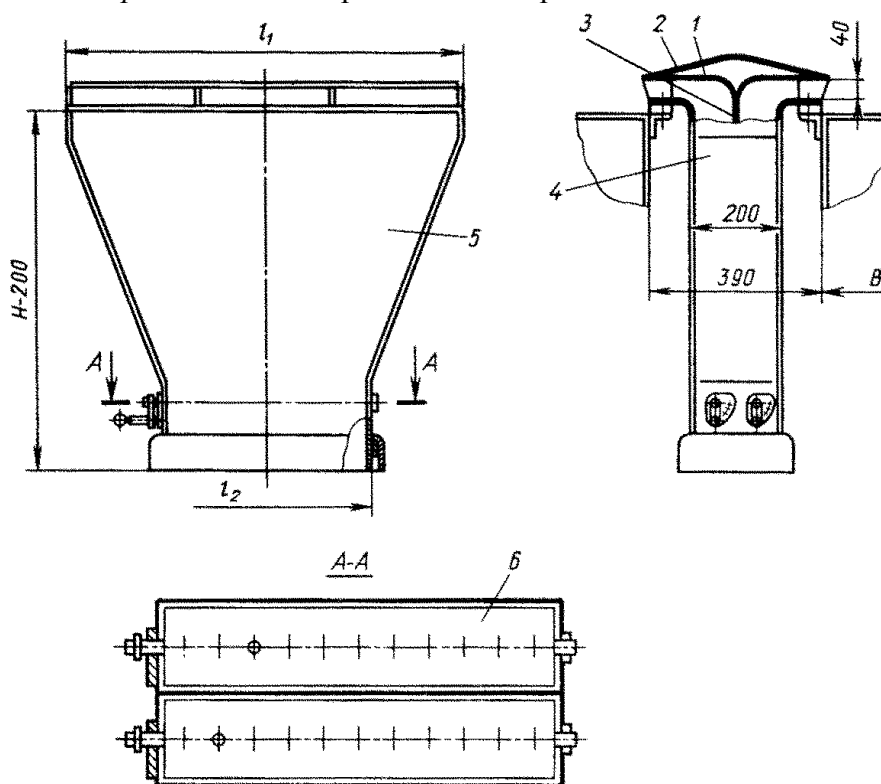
Двусторонний бортовой отсос с вертикальной щелью всасывания (обозначения размеров на рис.3): 1 – козырек; 2 – двухскатная крышка; 3 – перегородка; 4 – боковая стенка; 5 – стенка; 6 – шибер.
